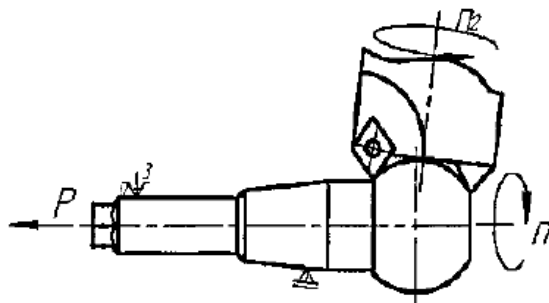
Схема фрезерування сферичної поверхні кульового пальця
